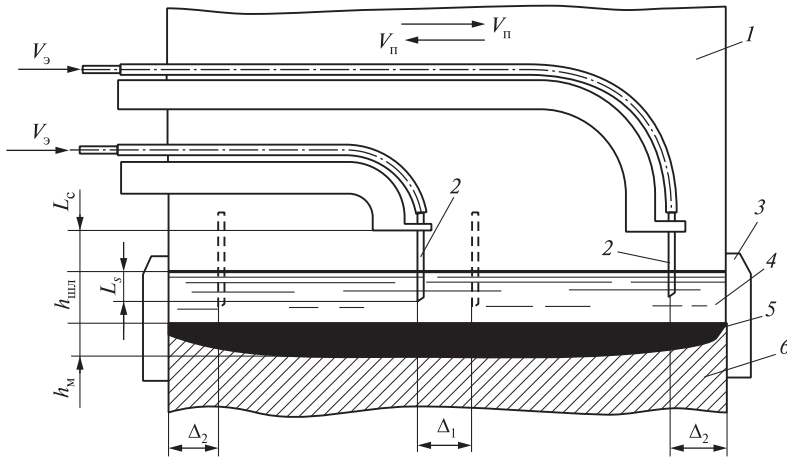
Схема электрошлаковой сварки:
